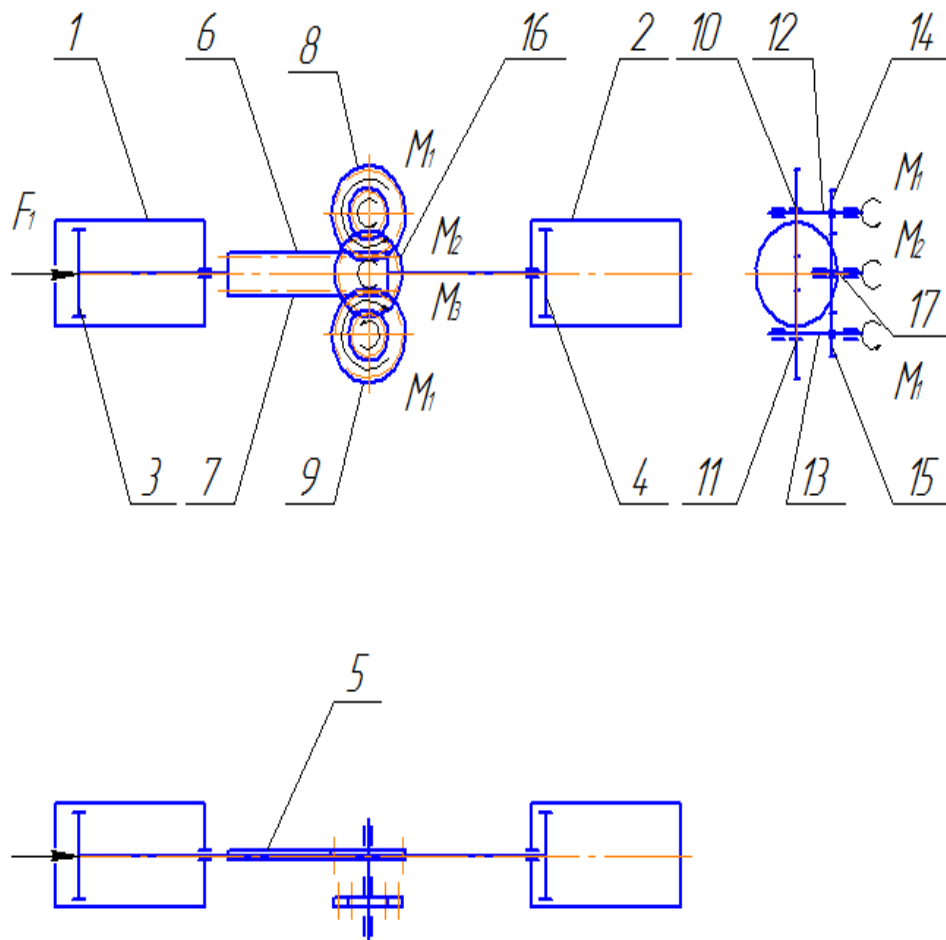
Схема двотактного поршневого опозитного двигуна при робочому ході першого циліндра: 1, 2 – циліндри; 3,4 – поршні; 5 - зубчаста рейка; 6, 7 – зубці; 8, 9 – шестерні; 10, 11 - обгінній муфті; 12, 13 - вали; 14, 15 - додаткові шестерні; 16 - центральне зубчасте колесо; 17 - вал
